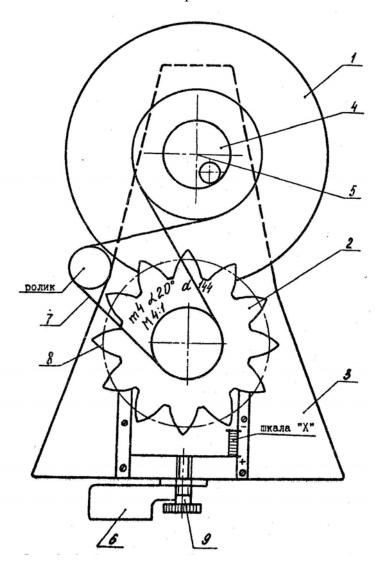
Схема прибора для построения эвольвентных профилей зубьев
